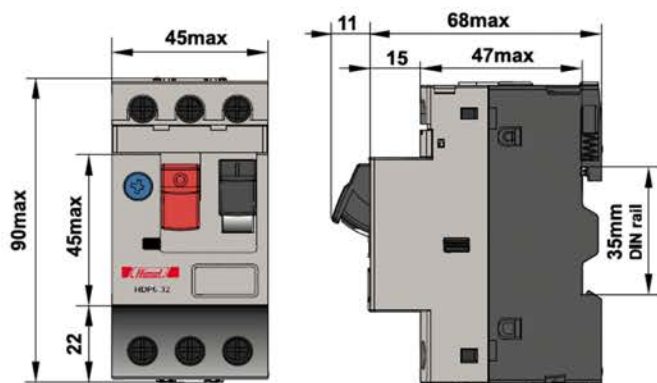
Габаритные и установочные размеры автоматических выключателей ВА-431, мм.
